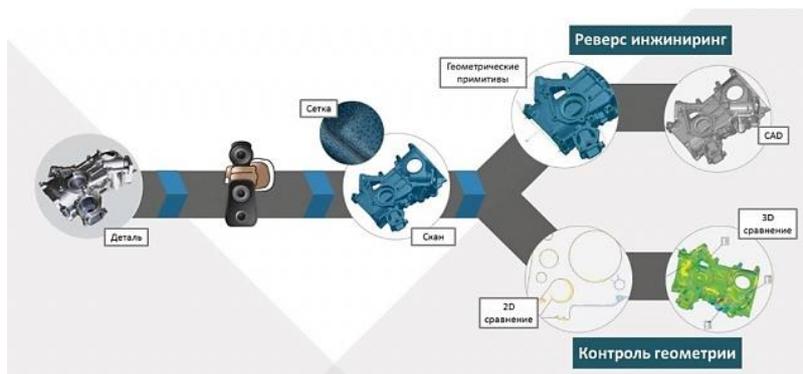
Реверс инжиниринг(reverse engineering) и контроль геометрии
